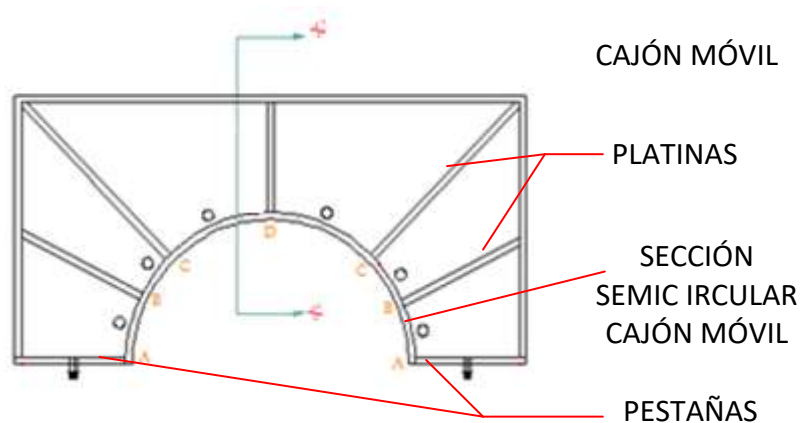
Esquema diseñado cajón móvil de la caja circular en planta. Disposición de platinas soldadas al cajón semicircular. Fuente: Propia
